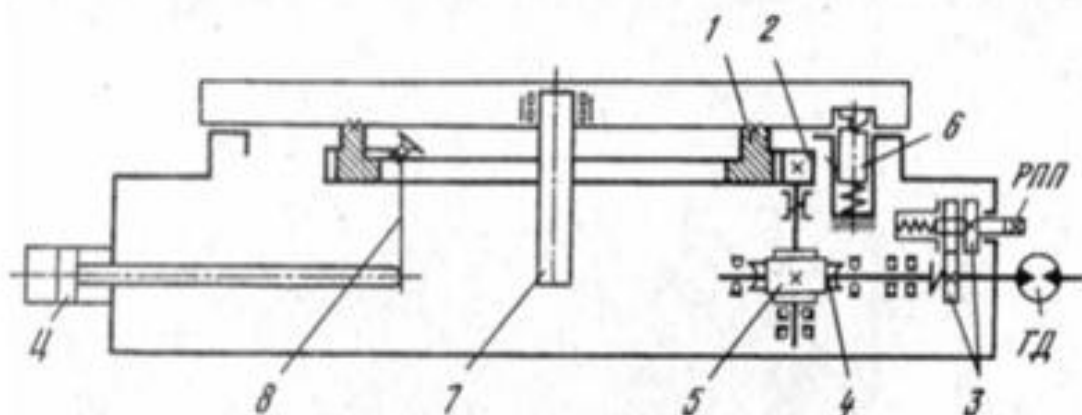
Кинематическая схема делительного стола с гидроприводом: ГД – гидродвигатель, Ц – цилиндр, РПП – ручной привод поворота планшайбы; 1 – зубчатый венец, 2 – приводная шестерня, 3 – колеса ручного привода, 4 – червячное колесо, 5 – червяк, 6 – фиксатор, 7 – центральная ось, 8 – рычаг зажима.
